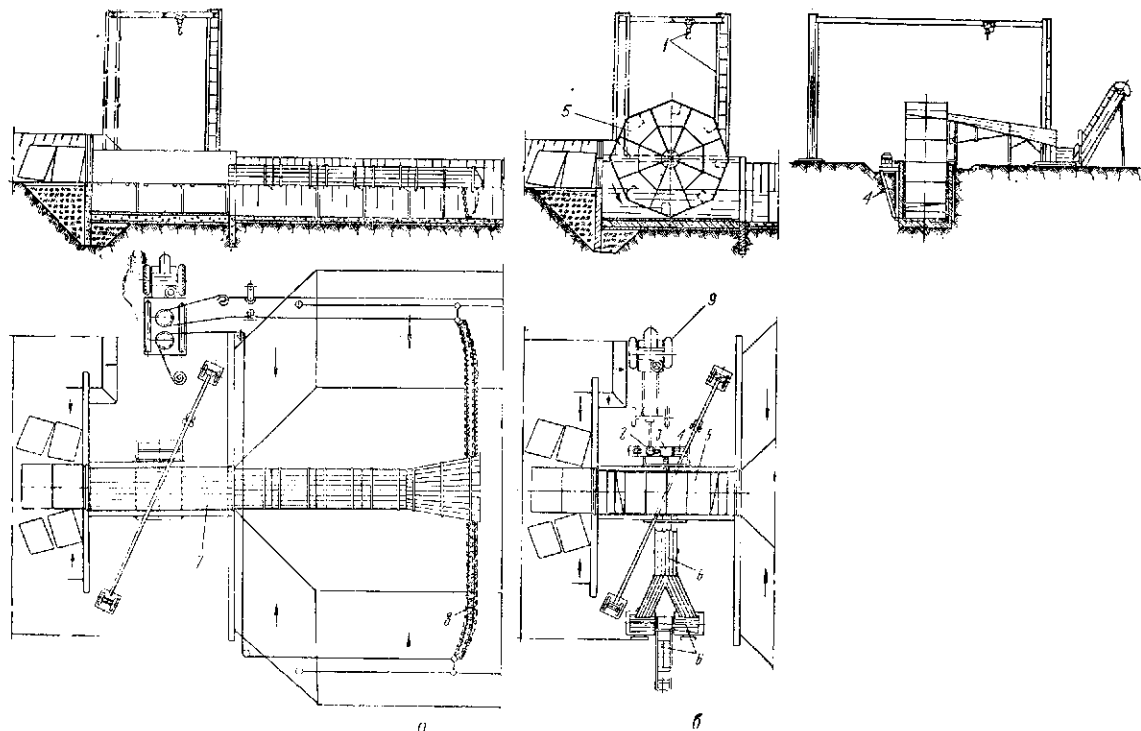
Роторный ковшовый рыбывыгрузатель: *а* — в момент приема и сортировки рыбы; *б* — при выгрузке из рыбоуловителя и погрузке рыбы в транспорт:
